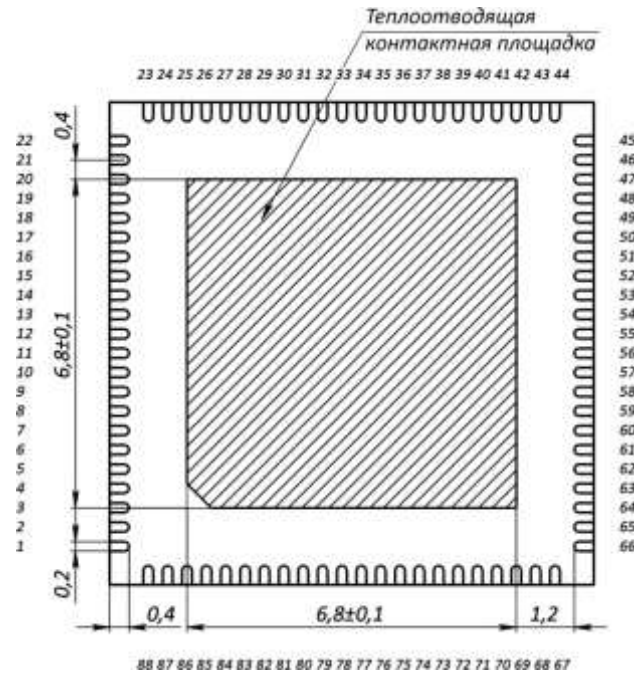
Габаритные размеры корпуса микроконтроллера (вид снизу)
